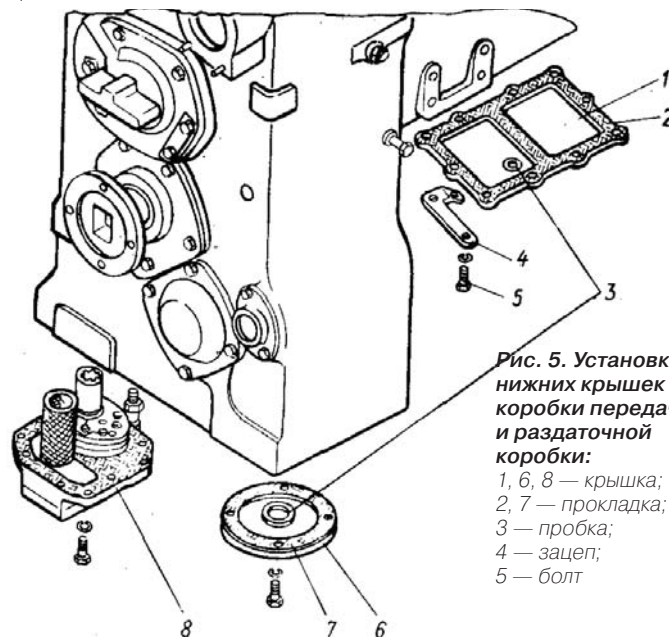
Установка нижних крышек коробки передач и раздаточной коробки:
